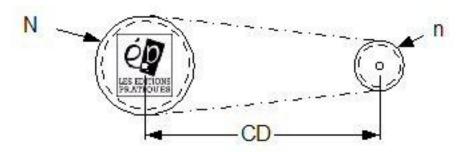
DIMENSION DE TRANSMISSION PAR CHAINE
